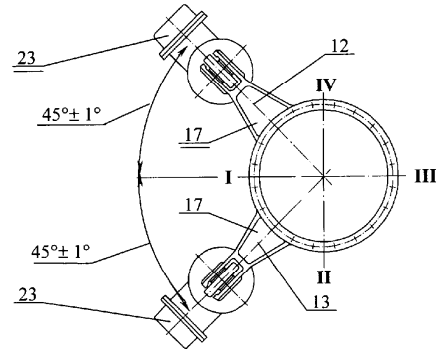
Общий вид сборочной единицы карданного подвеса без камеры:
